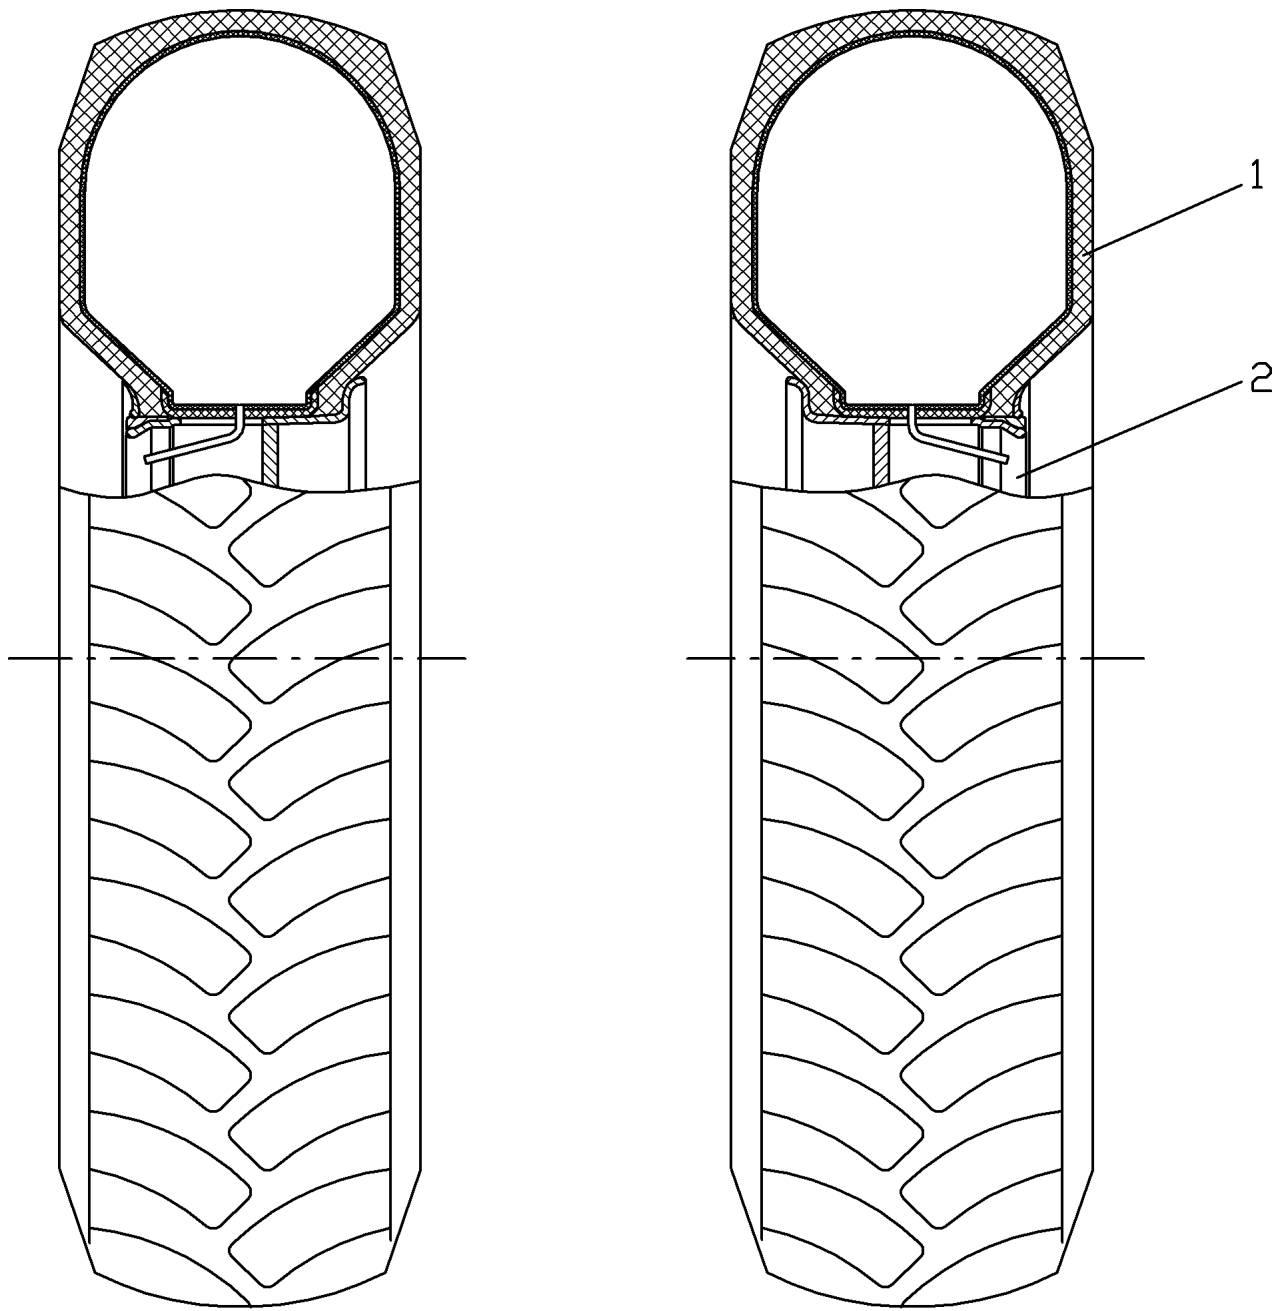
Колеса 723.03.01.02.000-01 и 723.03.01.01.000-01
